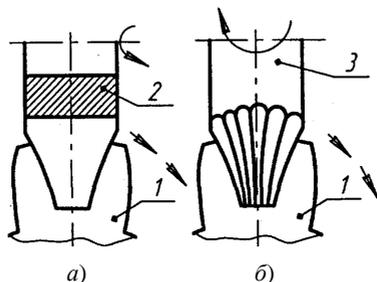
Пример фрезерования зубчатых колес модульными фрезами:
